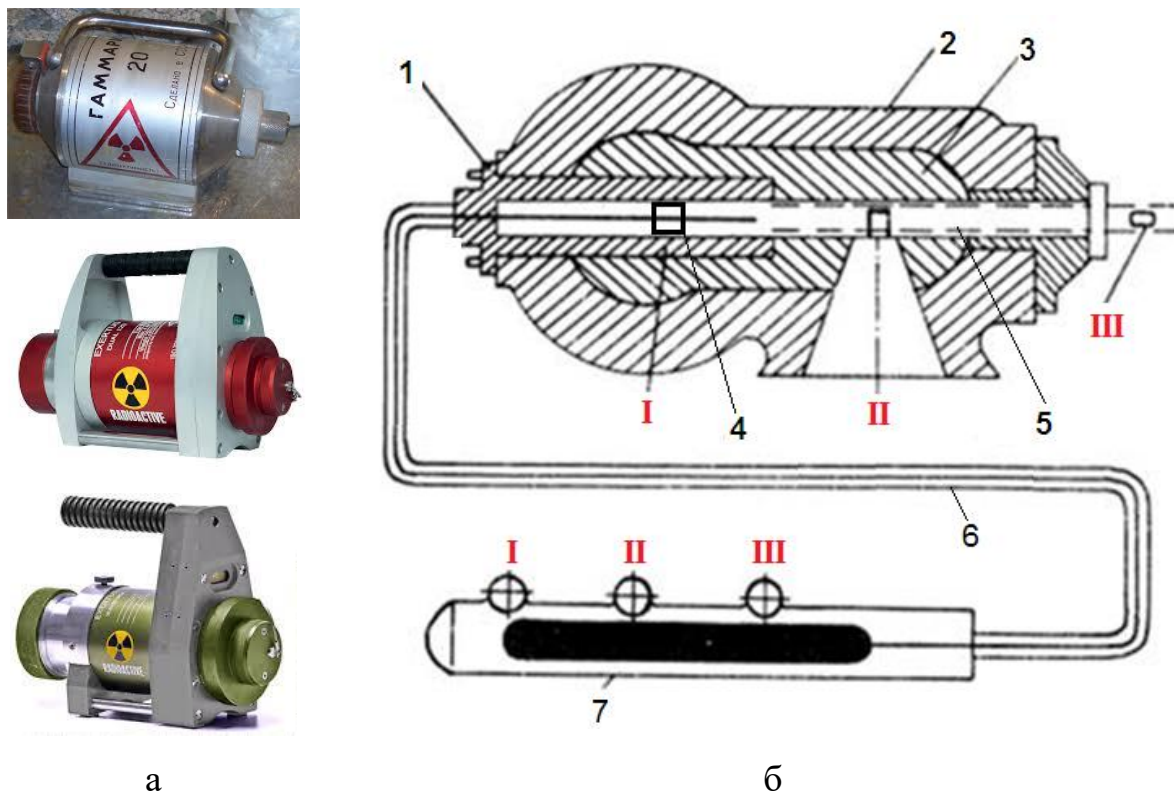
Загальний вигляд (а) та схема гама-дефектоскопу: 1 – свинцевий контейнер з ізотопом; 2 – чавунний кожух; 3 – свинець; 4 – напрямляюча голівка; 5 – ампулопровід; 6 – кабель дистанційного керування; 7 – пульт дистанційного керування: неробоче положення (I); робоче положення при просвічуванні спрямованим пучком (II); робоче положення при просвічуванні відкритою ампулою (III)
